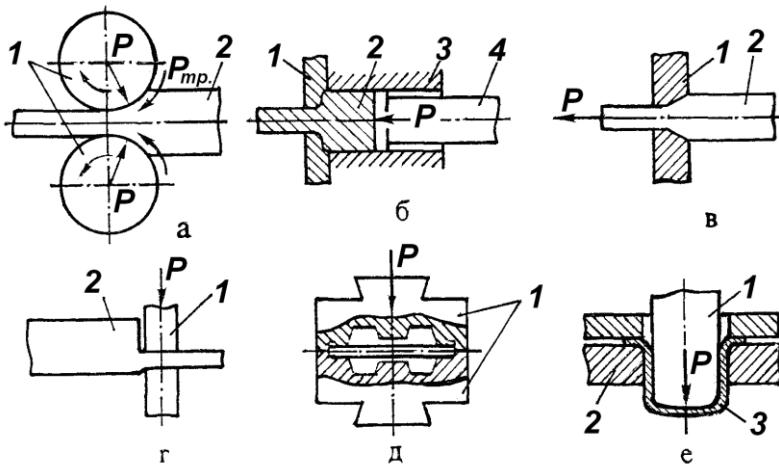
Схемы обработки металлов давлением: а – прокатка; б – прессование; в – волочение; г – ковка; д – объемная штамповка; е – листовая штамповка
